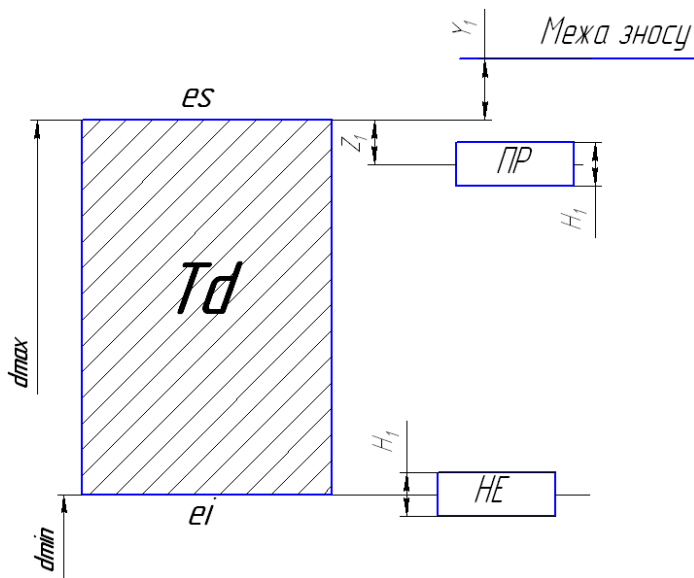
Схема полів допусків калібрів-скоб для контролю зовнішньої циліндричної поверхні втулки $\varnothing 30k6^{(+0,015)}_{(+0,002)}$
